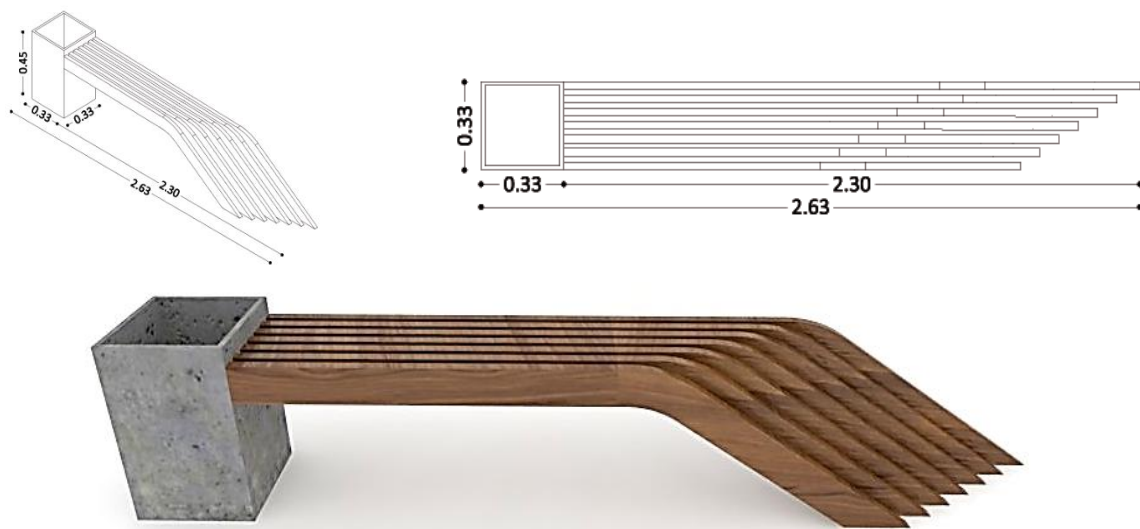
Planimetría y render, banca 2. Fuente: grupo de investigación.
